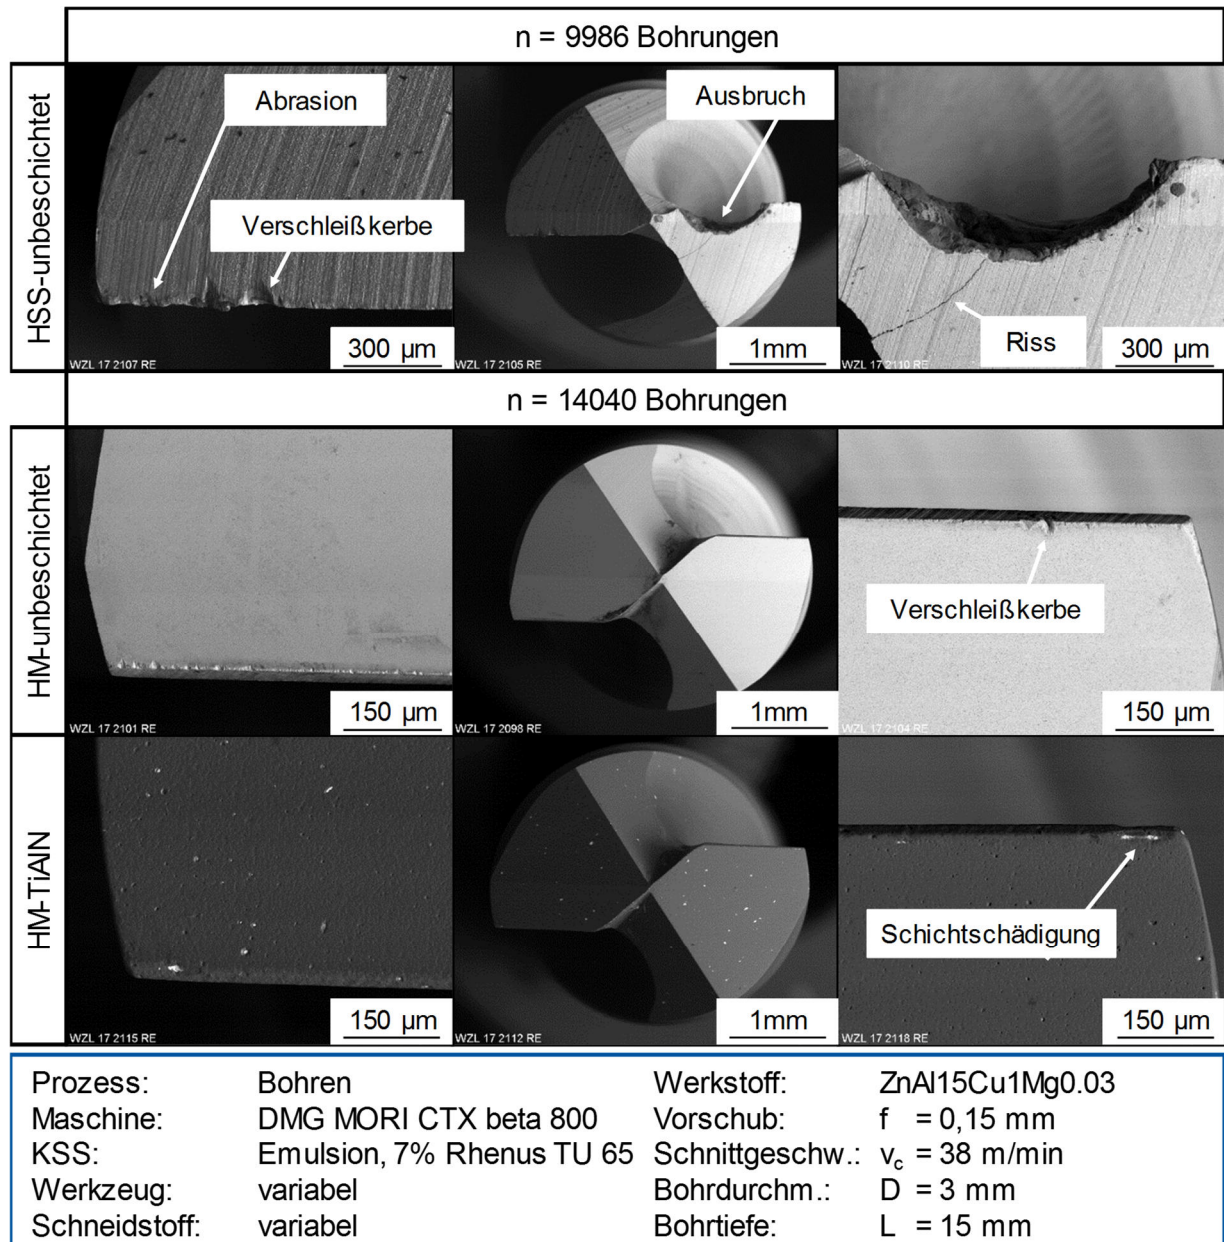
REM-Aufnahmen der Versuchswerkzeuge nach 9986 bzw. 14040 Bohrungen
